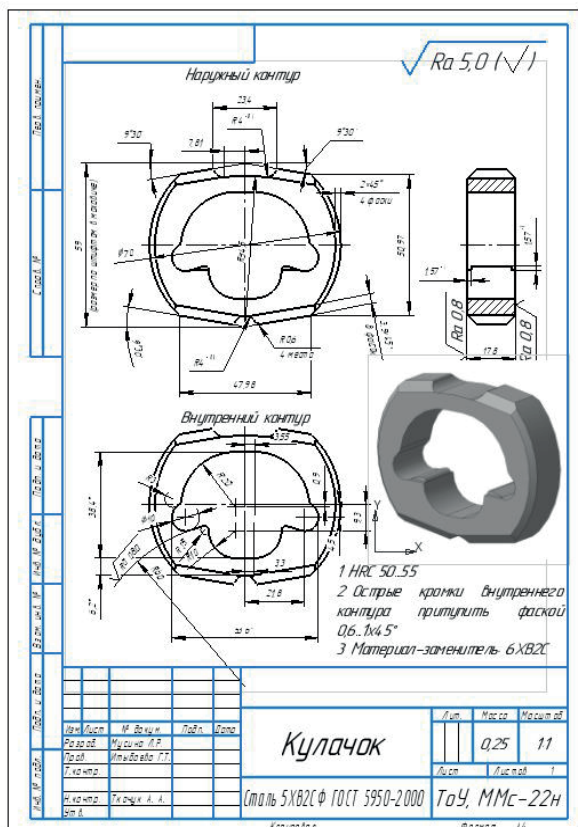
Рабочий чертёж детали «Кулачок»
